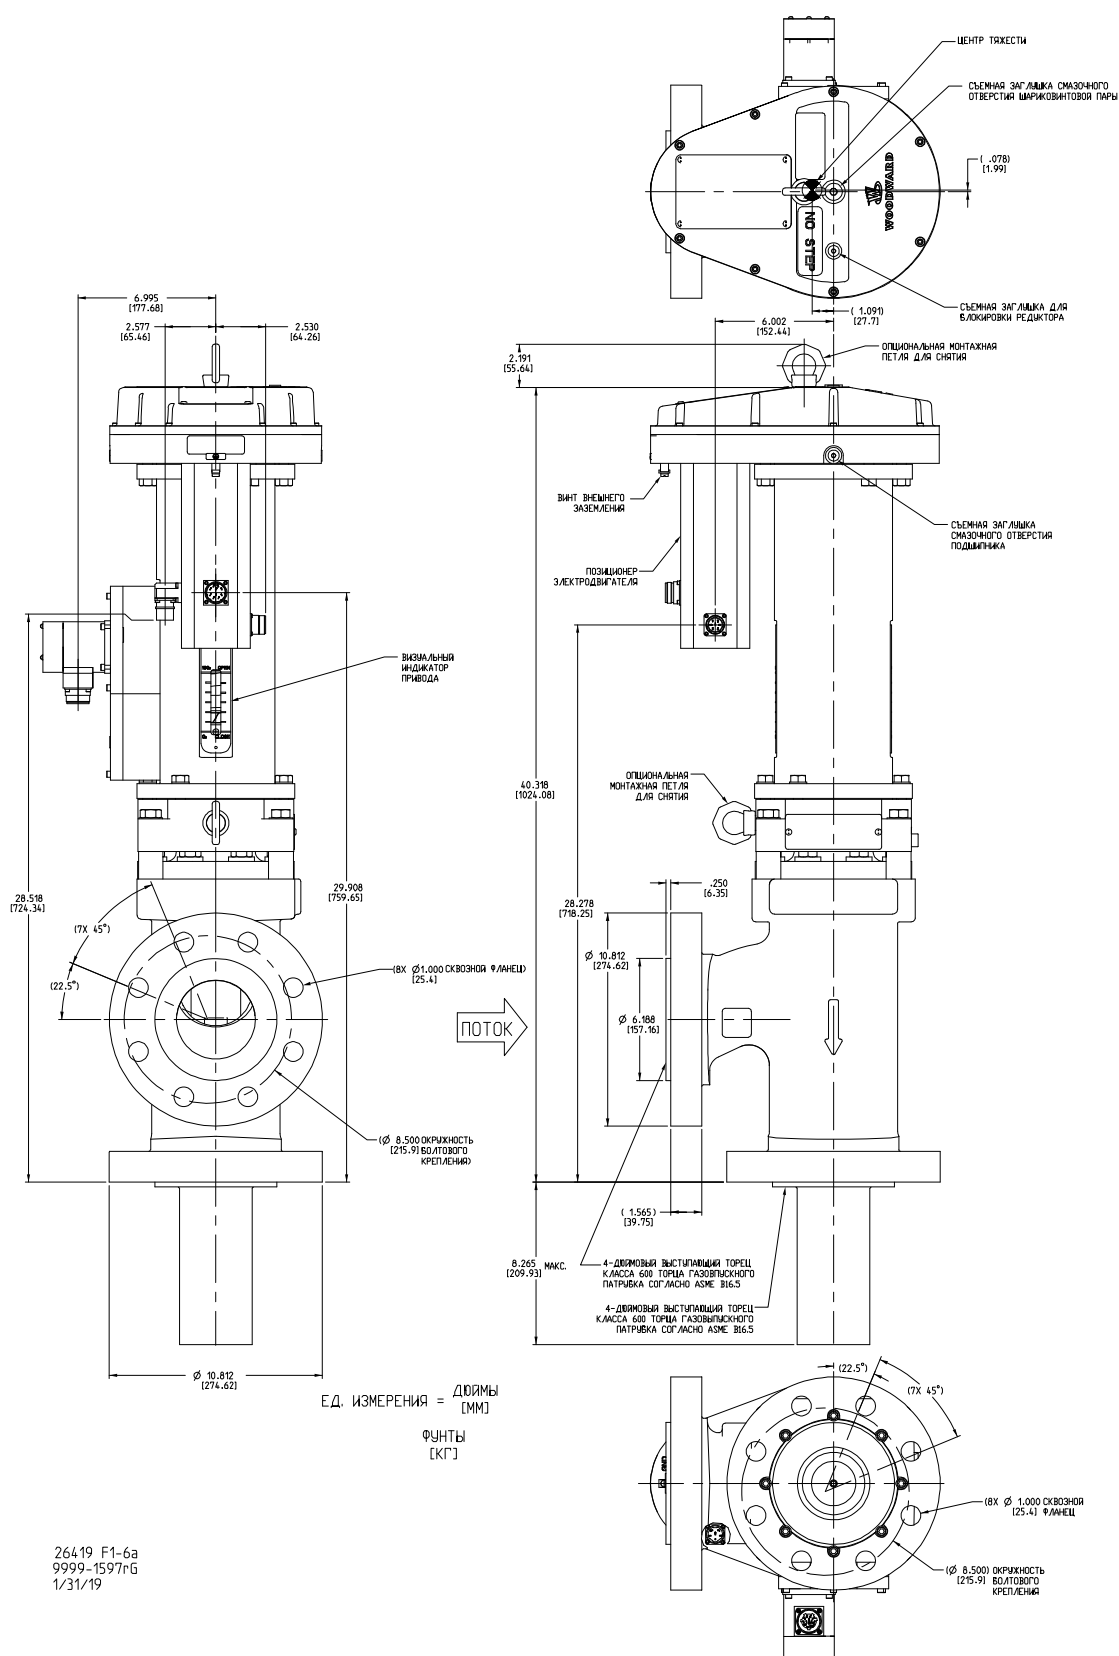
а. Габаритный чертеж (4-дюймовый клапан LESV класса 600)
